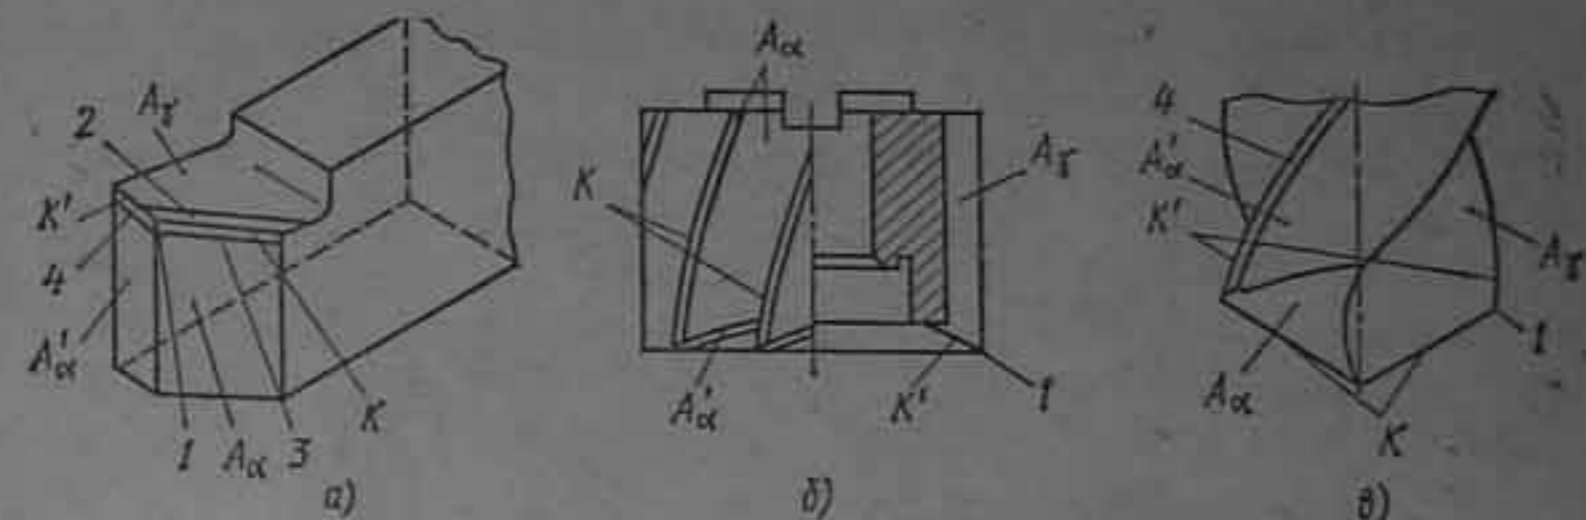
Геометрические элементы лезвия инструмента: а — токарный резец; б — торцовая фреза; в — сверло.  $A_v$  — передняя поверхность лезвия;  $K$  — главная режущая кромка;  $K'$  — вспомогательная режущая кромка;  $A_\alpha$  — главная задняя поверхность лезвия;  $A'_\alpha$  — вспомогательная задняя поверхность лезвия;  $I$  — вершина лезвия; 2 — фаска по передней поверхности; 3 — ленточка по главной задней поверхности; 4 — ленточка по вспомогательной задней поверхности
